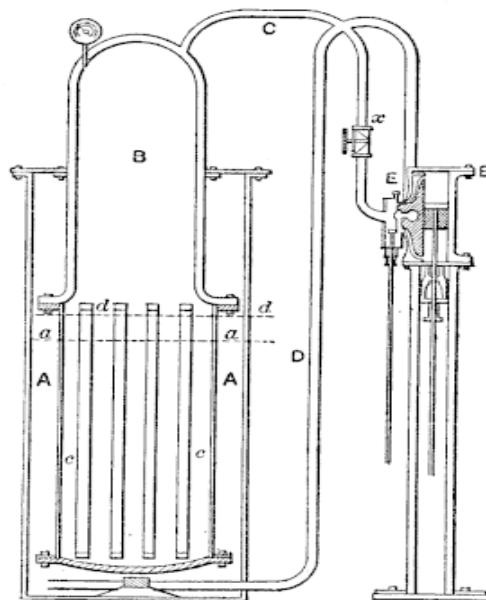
Machine à ammoniaque du Dr Lamb.
